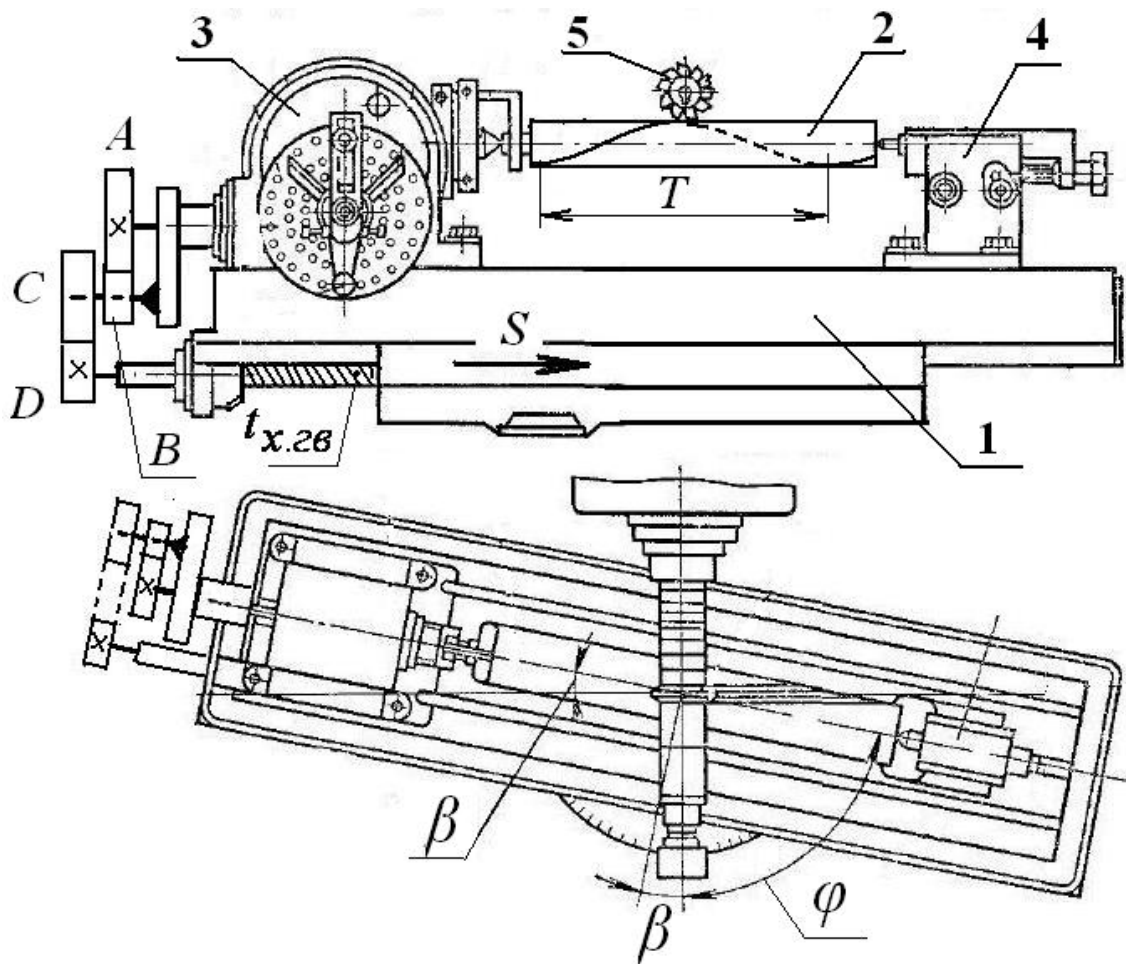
Схема нарізання спіральної канавки за допомогою УДГ на фрезерному верстаті
